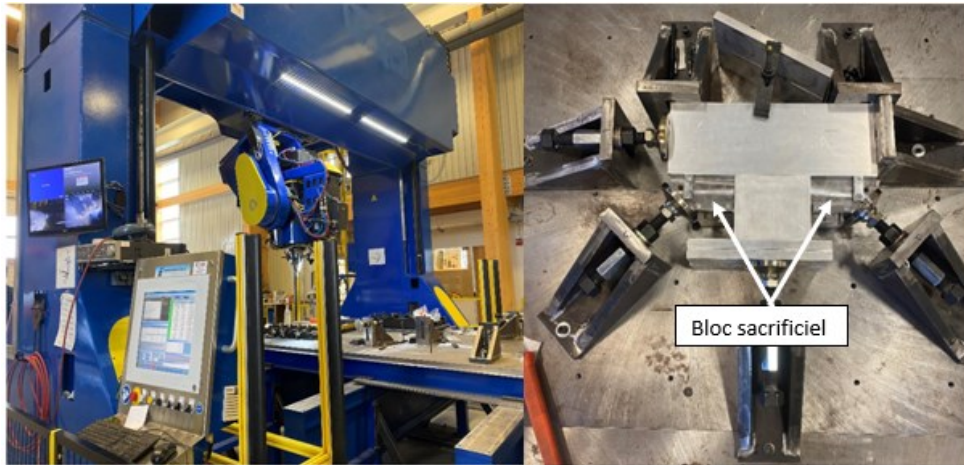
Machine et outils utilisés pour effectuer la soudure.
